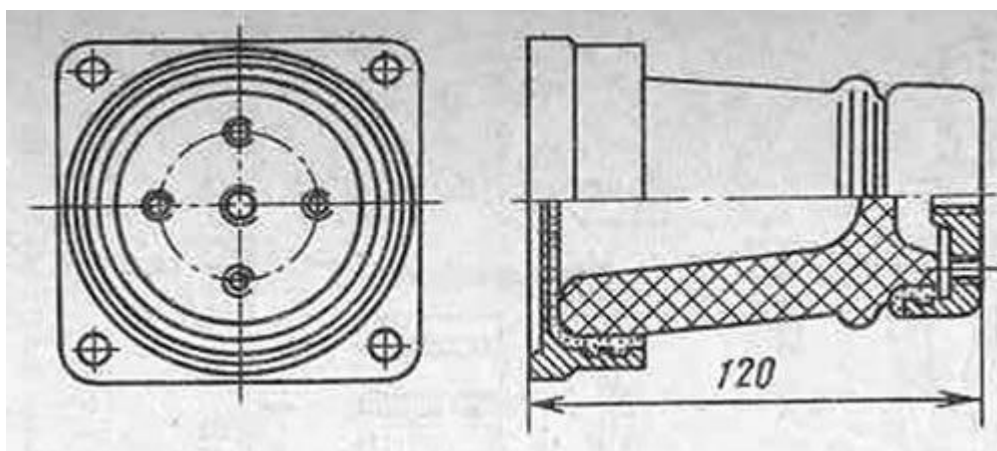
Опорный стержневой изолятор для внутренней установки серии ИО 10 кВ с квадратным фланцем и колпаком
